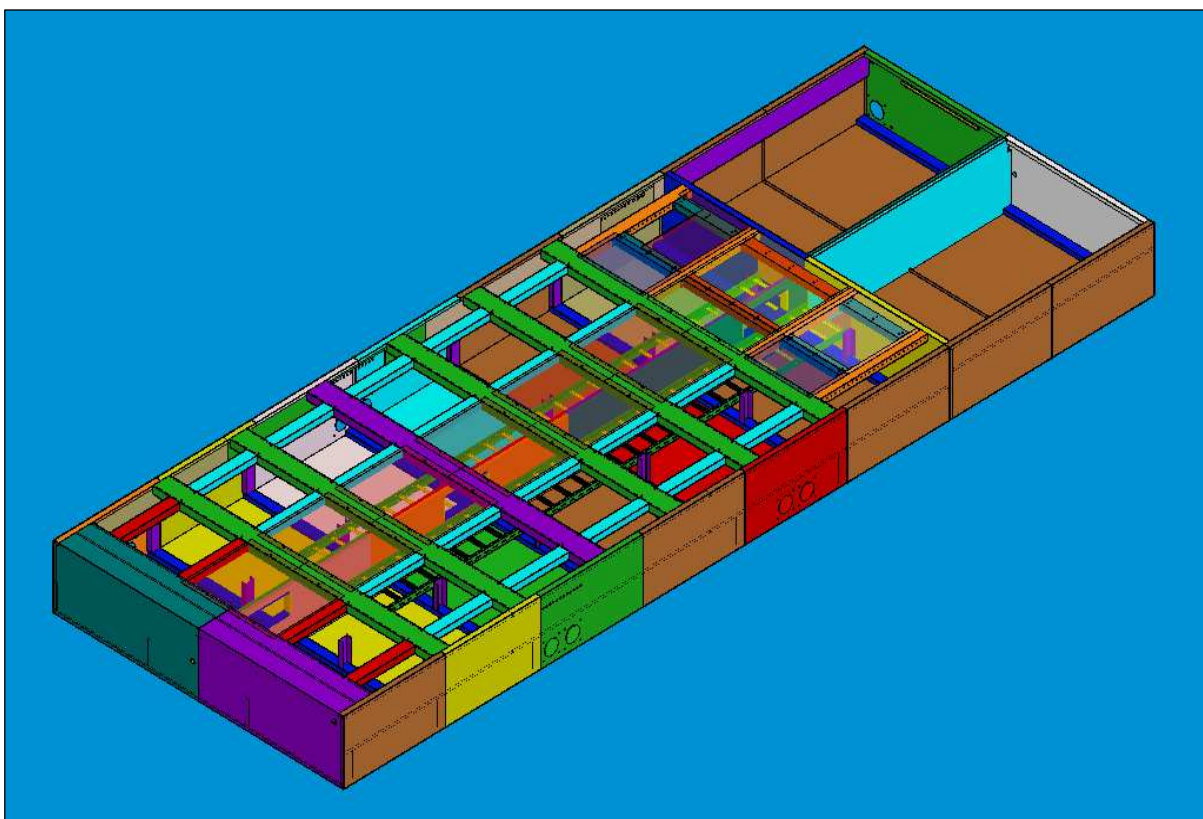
Model celkové sestavy v 3D CAD Solid Edge
